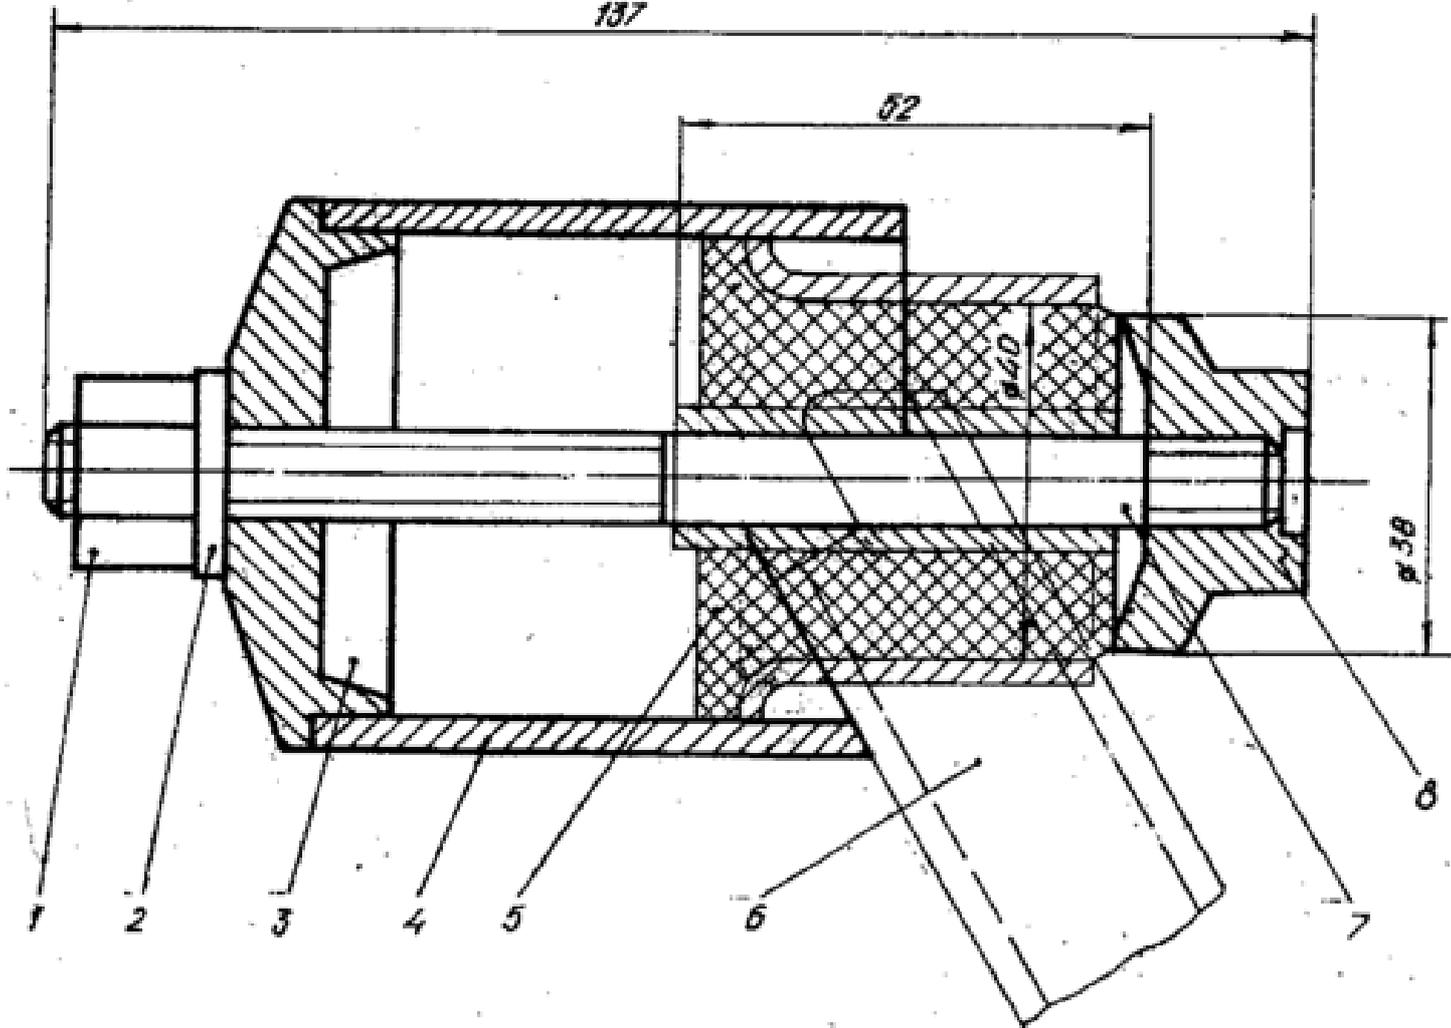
Выпрессовка сайлентблока из рычага балки передней подвески: 1 - гайка; 2 - шайба; 3 - крышка стакана; 4 - стакан; 5 - сайлентблок; 6 - рычаг задней подвески; 7 - винт; 8 - толкатель.
